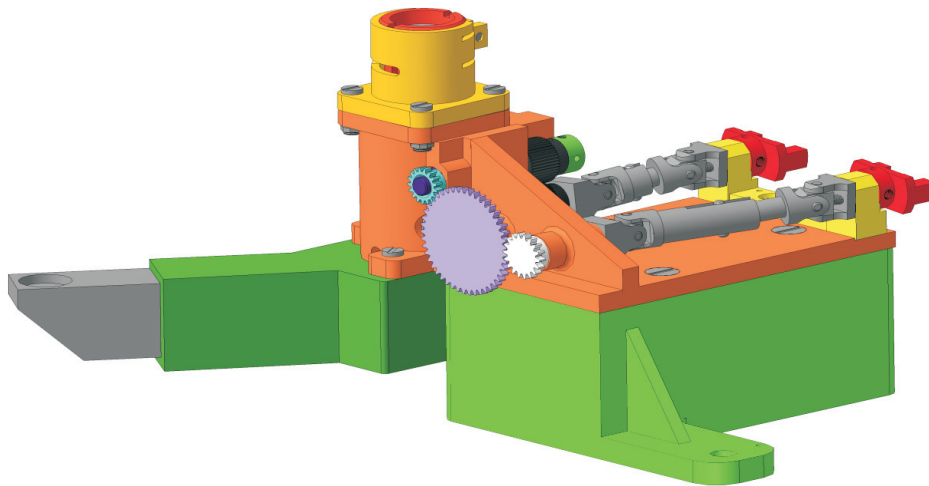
3D-прототип под сборки механизма выверки визира мехатронного прибора
